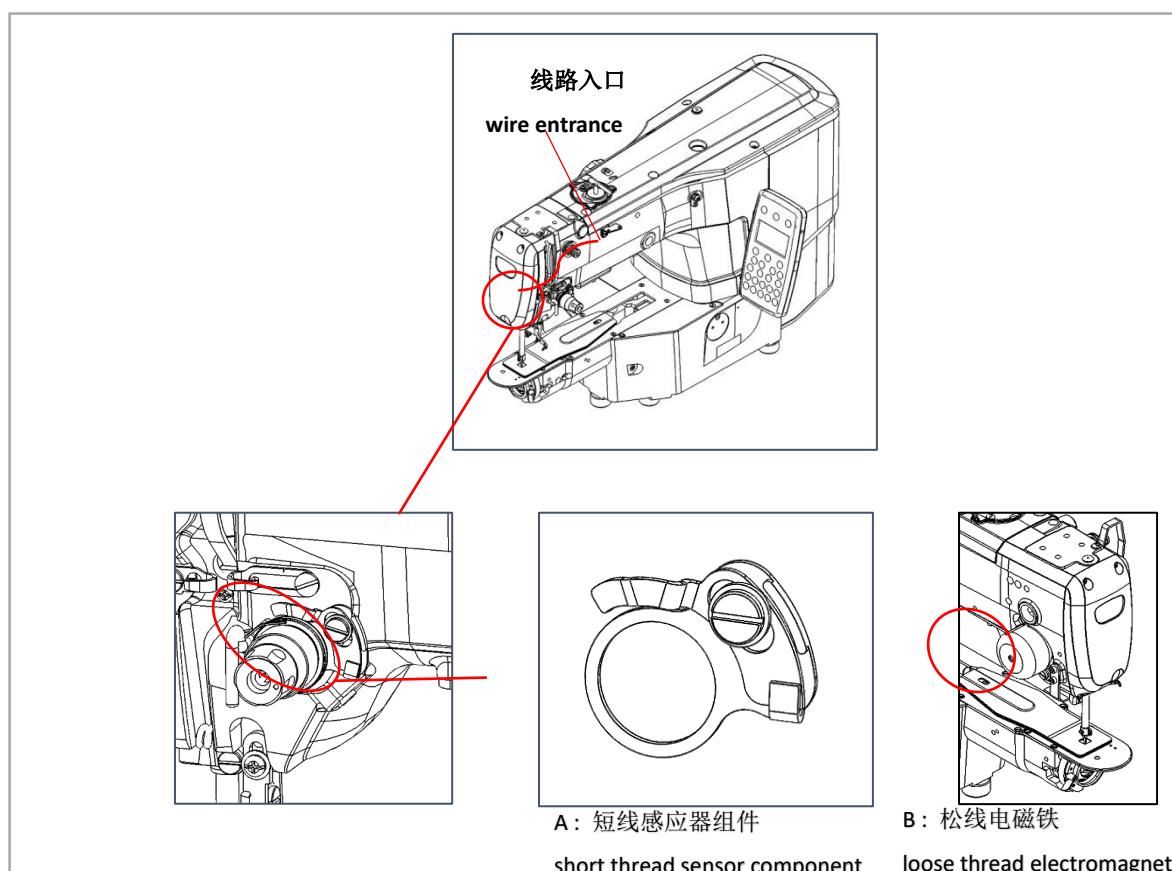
短线感应器安装 Figure 9.6 Installation of Short Thread Sensor
